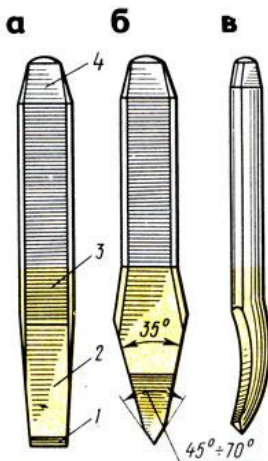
Инструменты для рубки: а - зубило, б - крейцмейсель, в - канавочник
